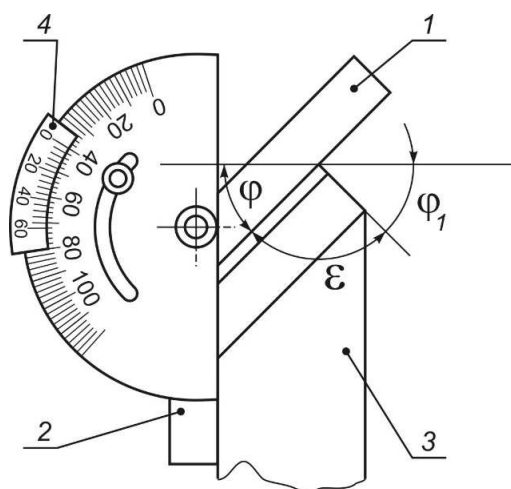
Схема измерения угла в плане универсальным угломером
